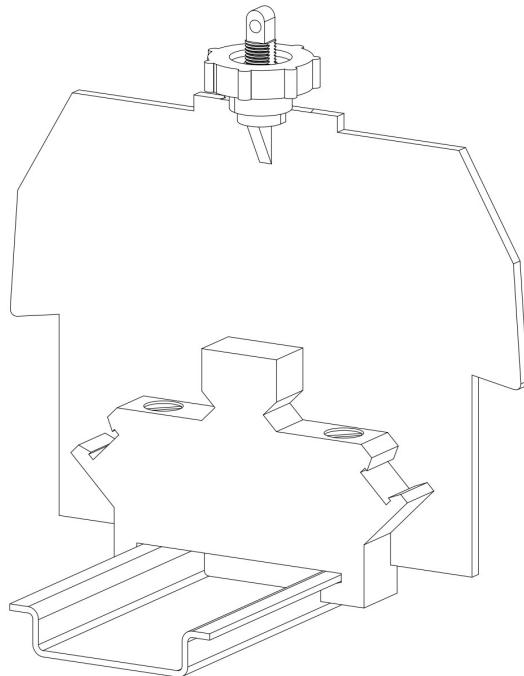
установленный держатель защитного профиля со специальной ножкой
